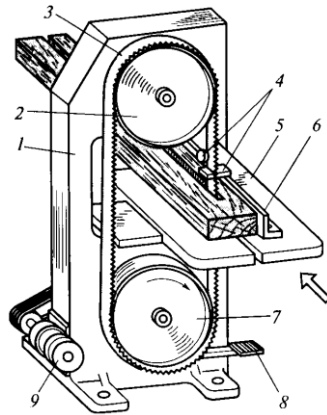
Стрічкопилковий столярний верстат: 1 – станина; 2 – верхній неприводний шків; 3 – пилка; 4 – напрямний пристрій; 5 – стіл; 6 – базувальна лінійка; 7 - приводний шків; 8 - педаль гальма; 9 - електродвигун
